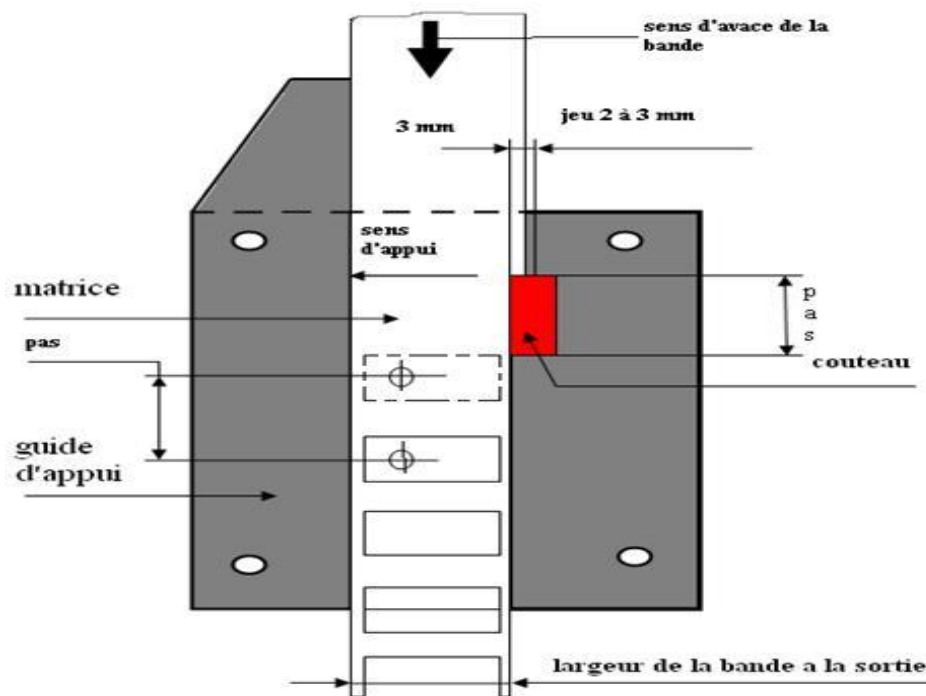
Principe de l'Outil à Contre-Plaque à Engrenage.
